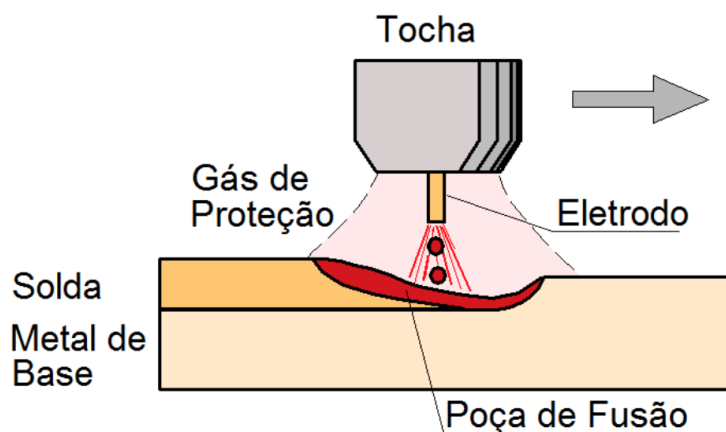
Representação esquemática do processo de soldagem GMAW [7].
